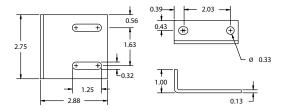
Accesorio de montaje para el sensor a prueba de explosiones
